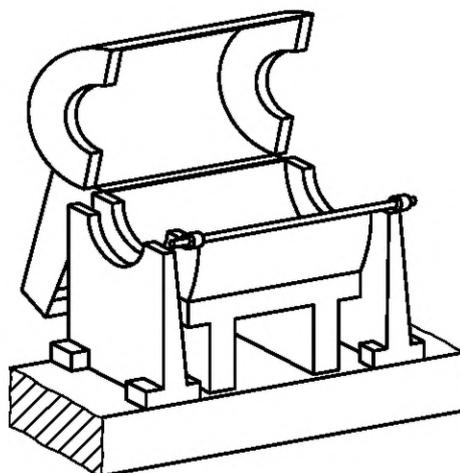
Кожух ротора для горизонтального балансирующего станка
